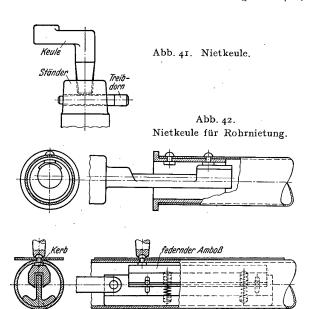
Zwei-Mann-Nietwerkzeug für Innennietung
